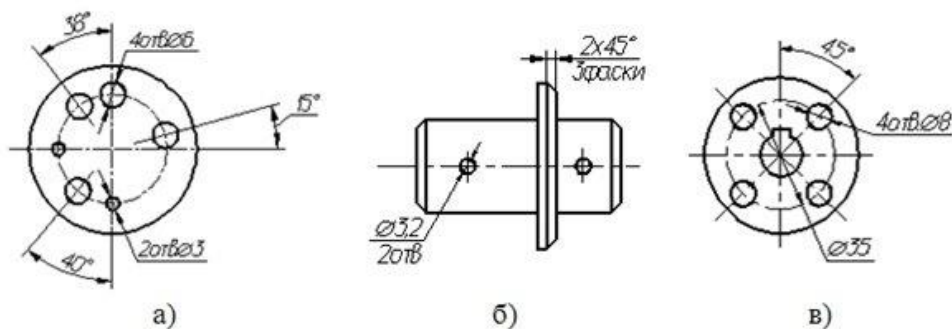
Примеры нанесения размеров одинаковых отверстий
